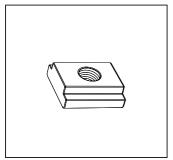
ÉCROU COULISSANT EN T (REF. YXW-0003-000)
